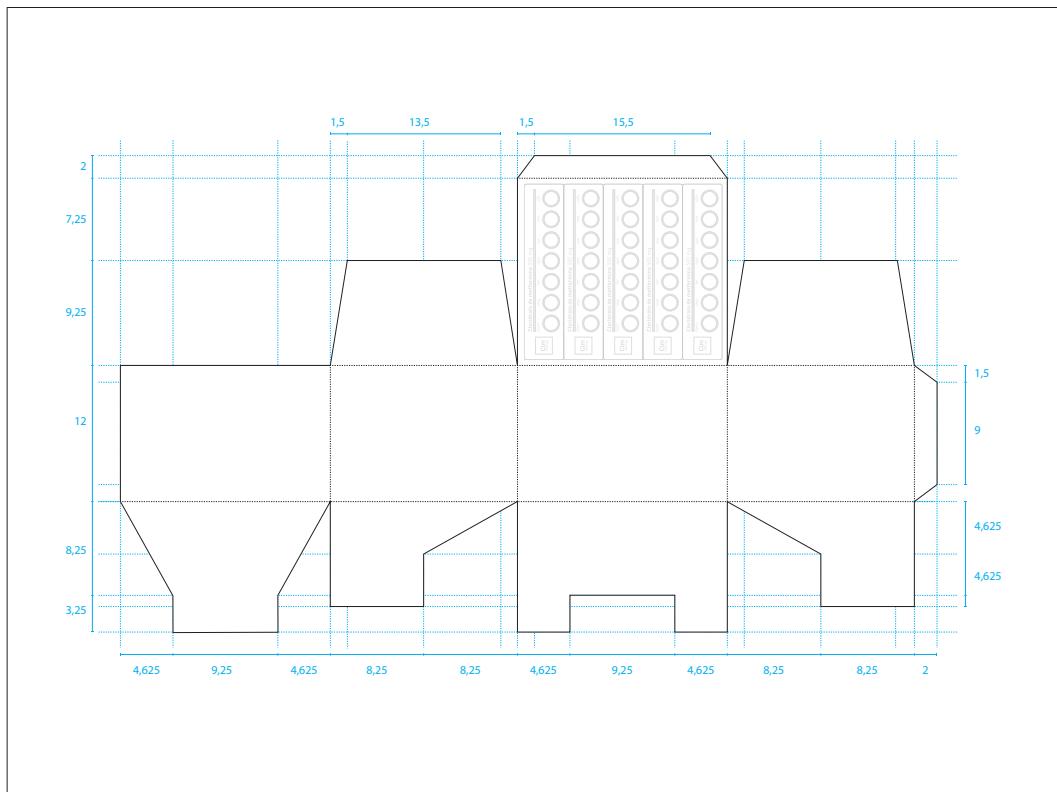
Planimetria da caixa de fornecimento do blister maior (Padrão 4).
